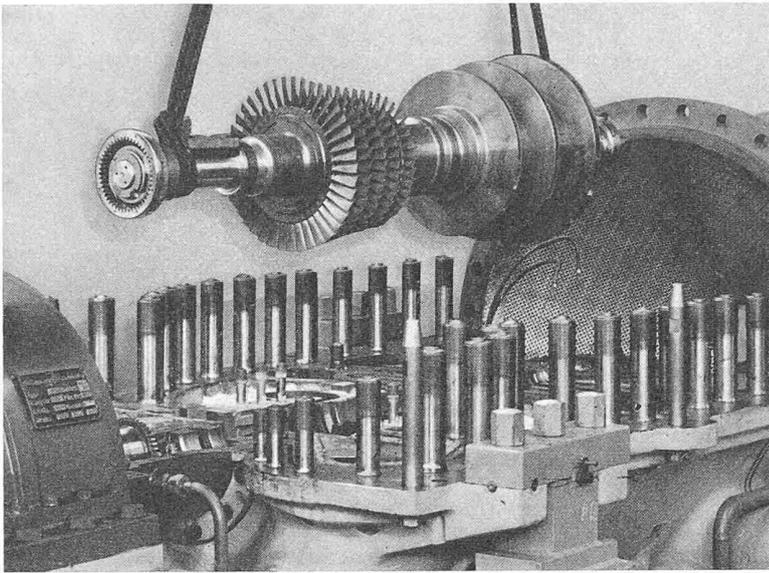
Kompressor-Turbinenrotor, links Turbinenläufer mit fünf Stufen, rechts dreistufiger Radialkompressor. Unten ist das offene Maschinengehäuse mit Reduktionsgetriebe links und Vorkühler rechts sichtbar
